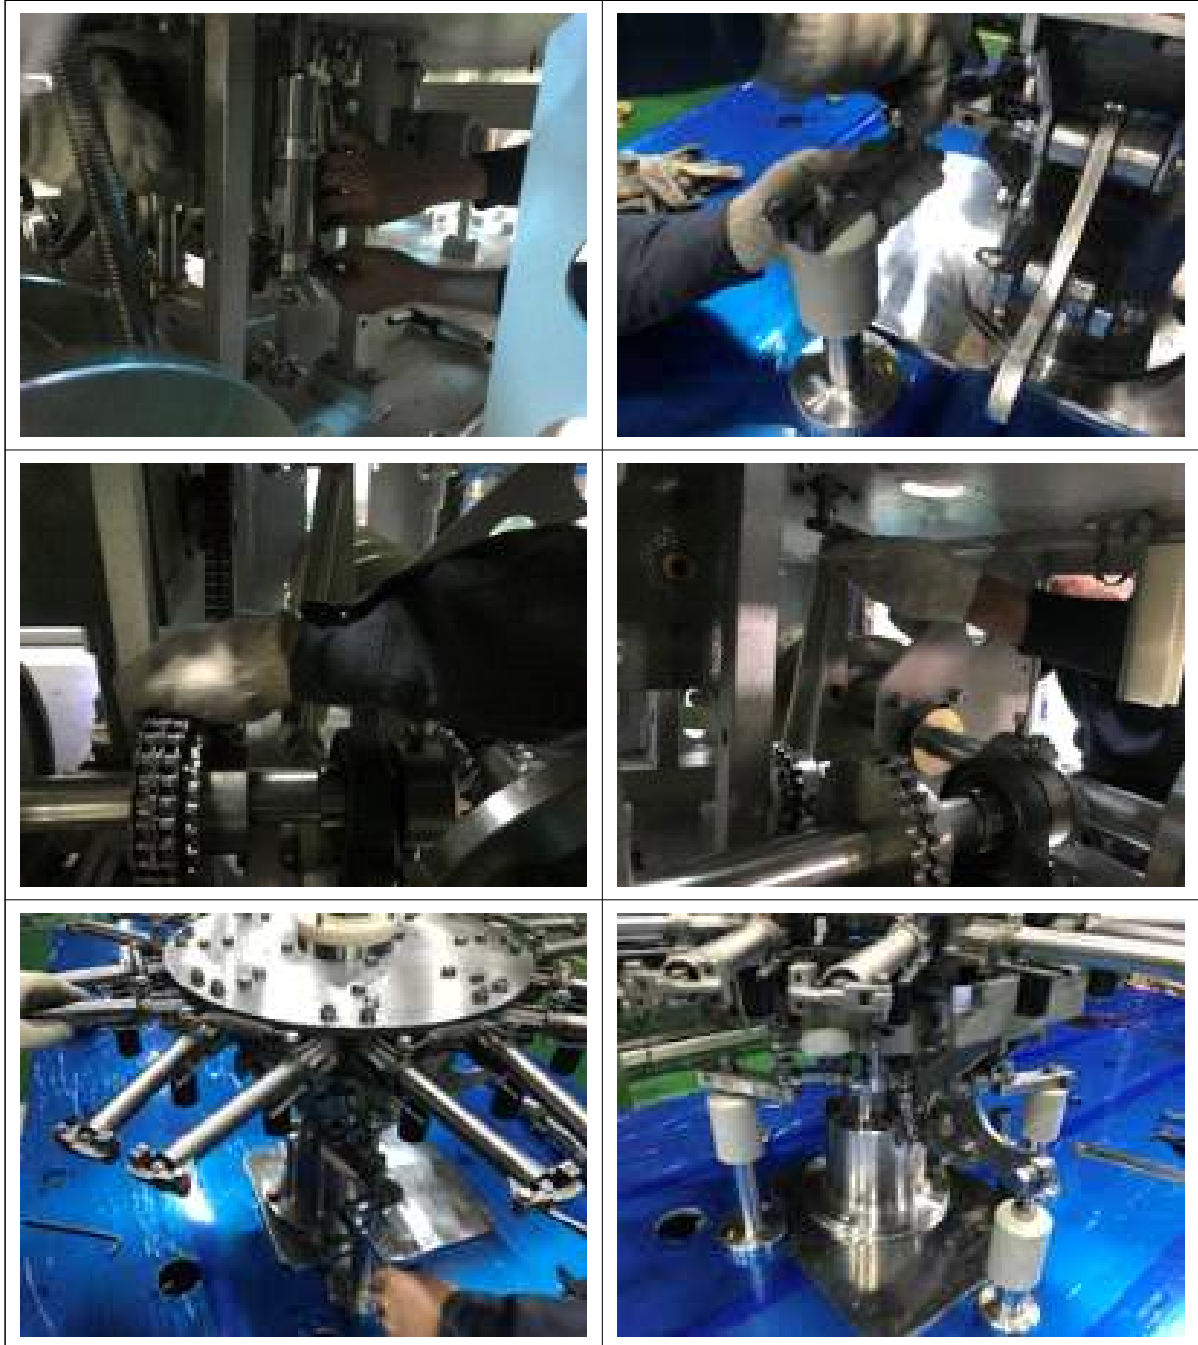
Gripper 운영을 위해 하부 Cam 및 실린더 연동 작업
